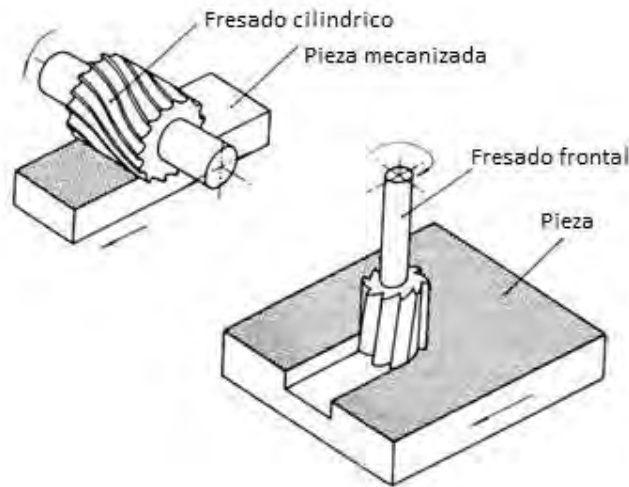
Fresado tangencial o cilíndrico (izquierda) y fresado frontal (derecha) [10].
